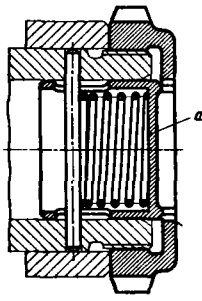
Стопорение кольцевой гайки пружинным фиксатором
